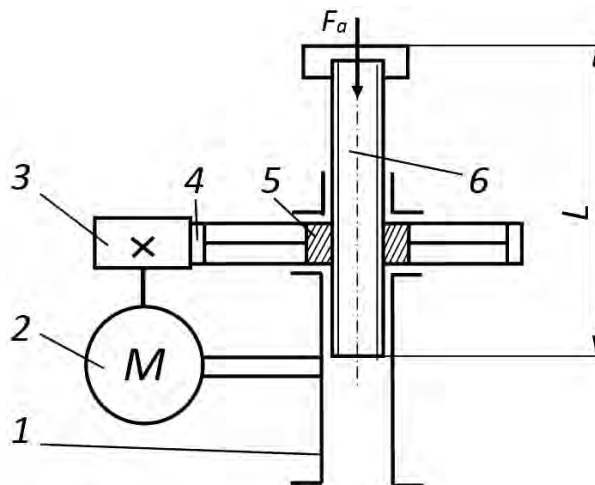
Кинематическая схема подъемного механизма: 1 – стойка; 2 – электродвигатель; 3 – шестерня; 4 – зубчатое колесо; 5 – гайка; 6 – винт
